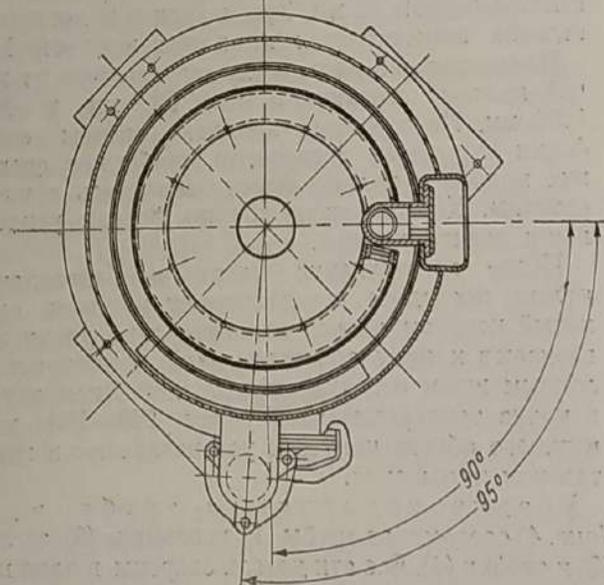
Общий вид газогенератора ЗИС-21 с топливником УТВ-2
